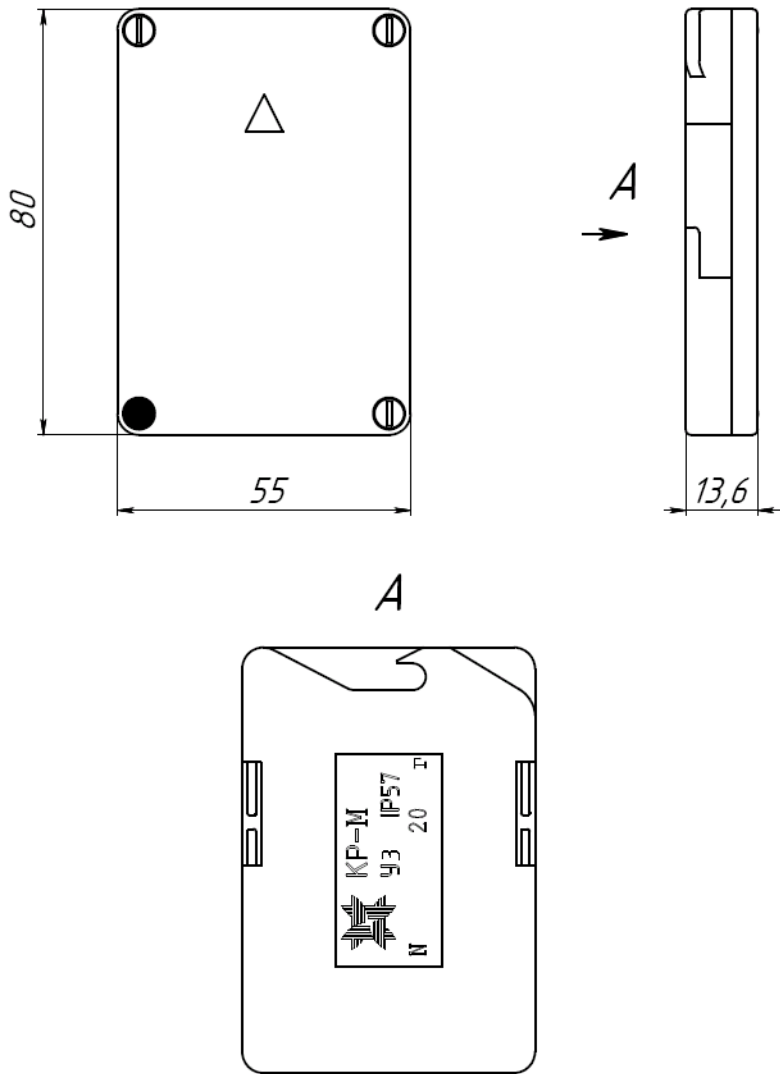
Внешний вид и габаритные размеры кассеты регистрации KP-M 36993-360-00-01
